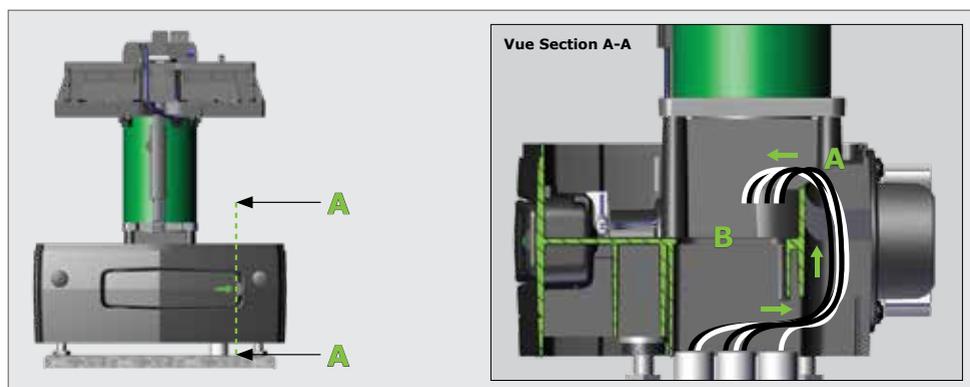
CHEMINEMENT DES CABLES POUR RENOVATION AVEC DES CABLES PLUS LONGS
